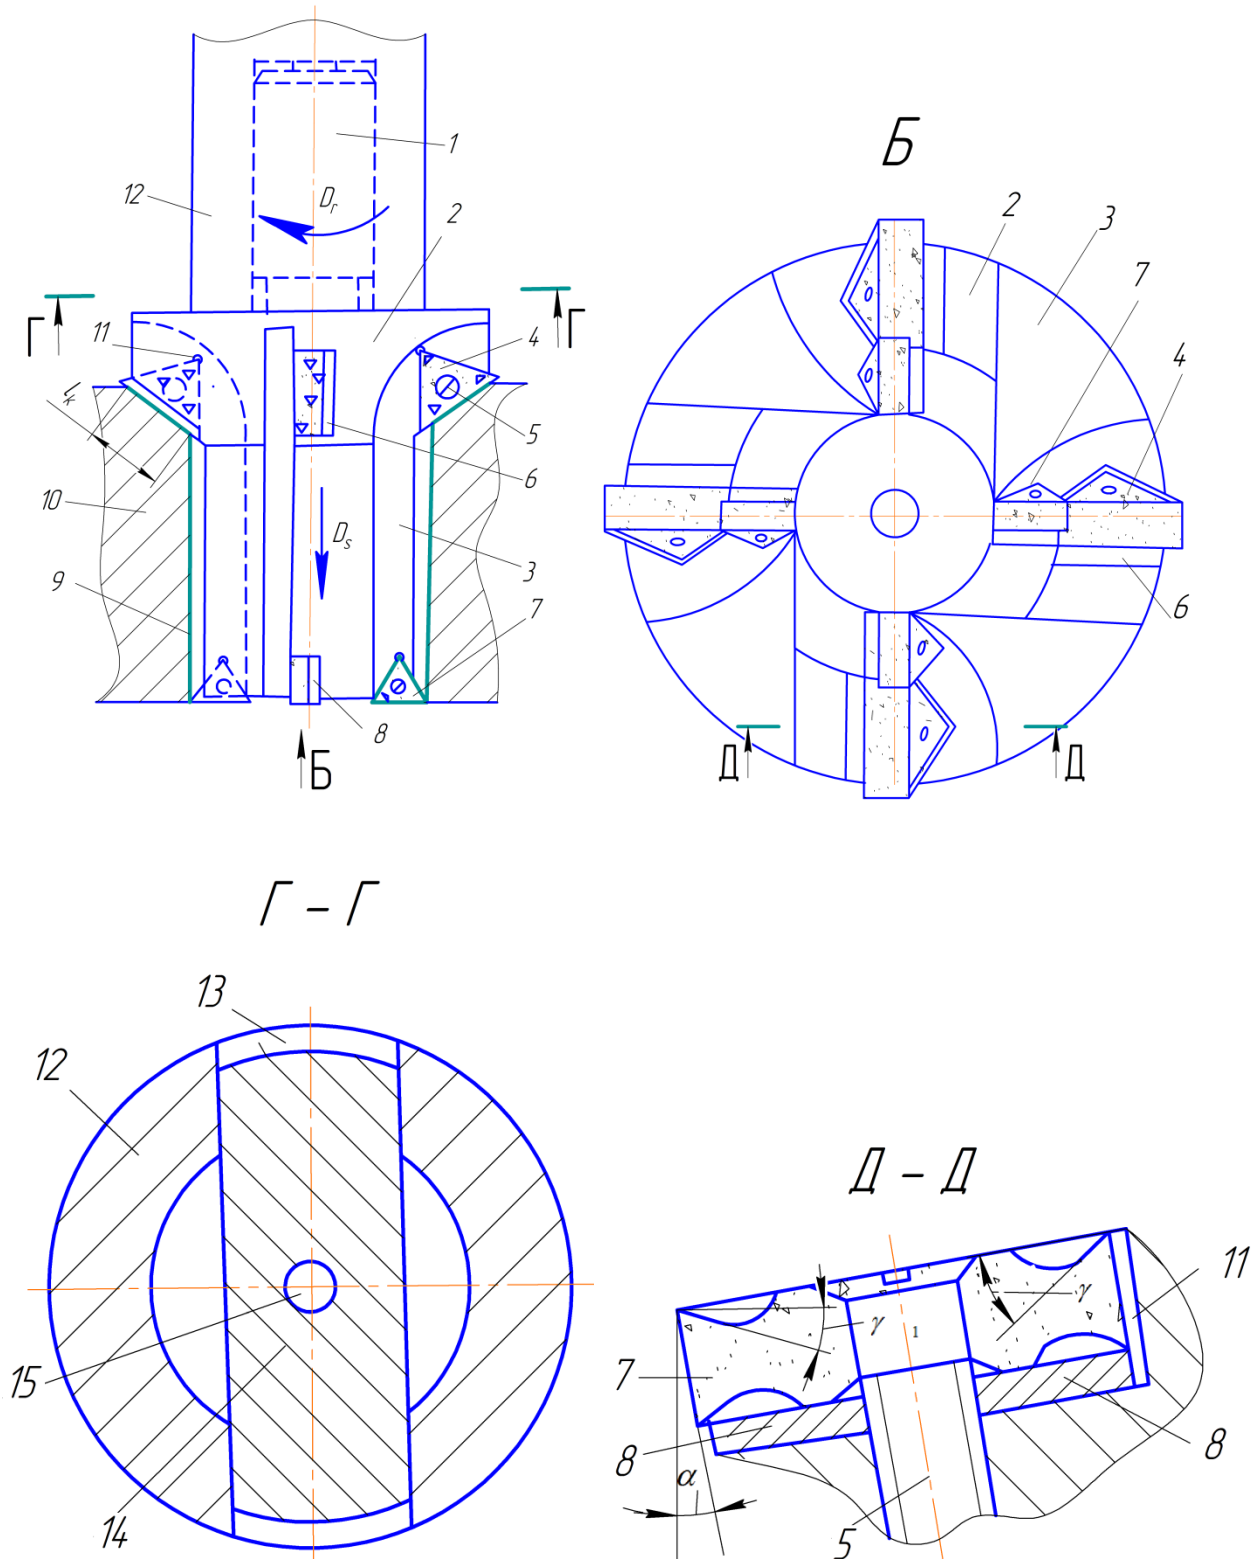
Конструкция комбинированного зенкера и схема обработки наплавленных поверхностей:
